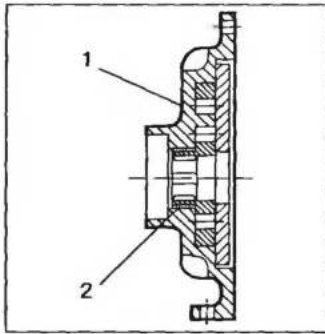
Ремонт сопряжения внутренней шестерни и корпуса масляного насоса:
